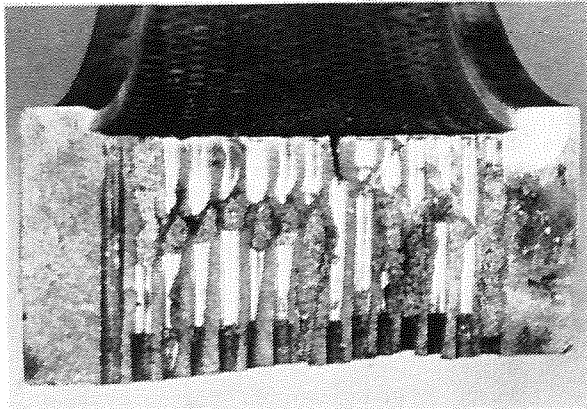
Aspecto superficial de la fractura de la matriz. En la parte superior derecha pueden apreciarse las señales de la grieta que ha causado la rotura (x 0,5).
